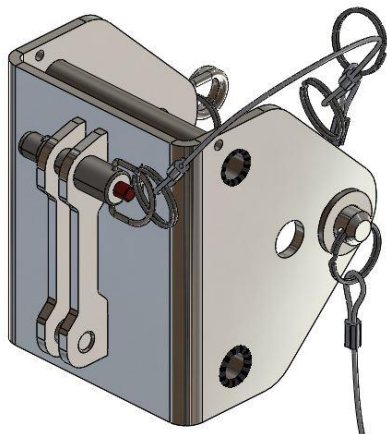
Universal-Windenhalterung PAD100-301-000.
